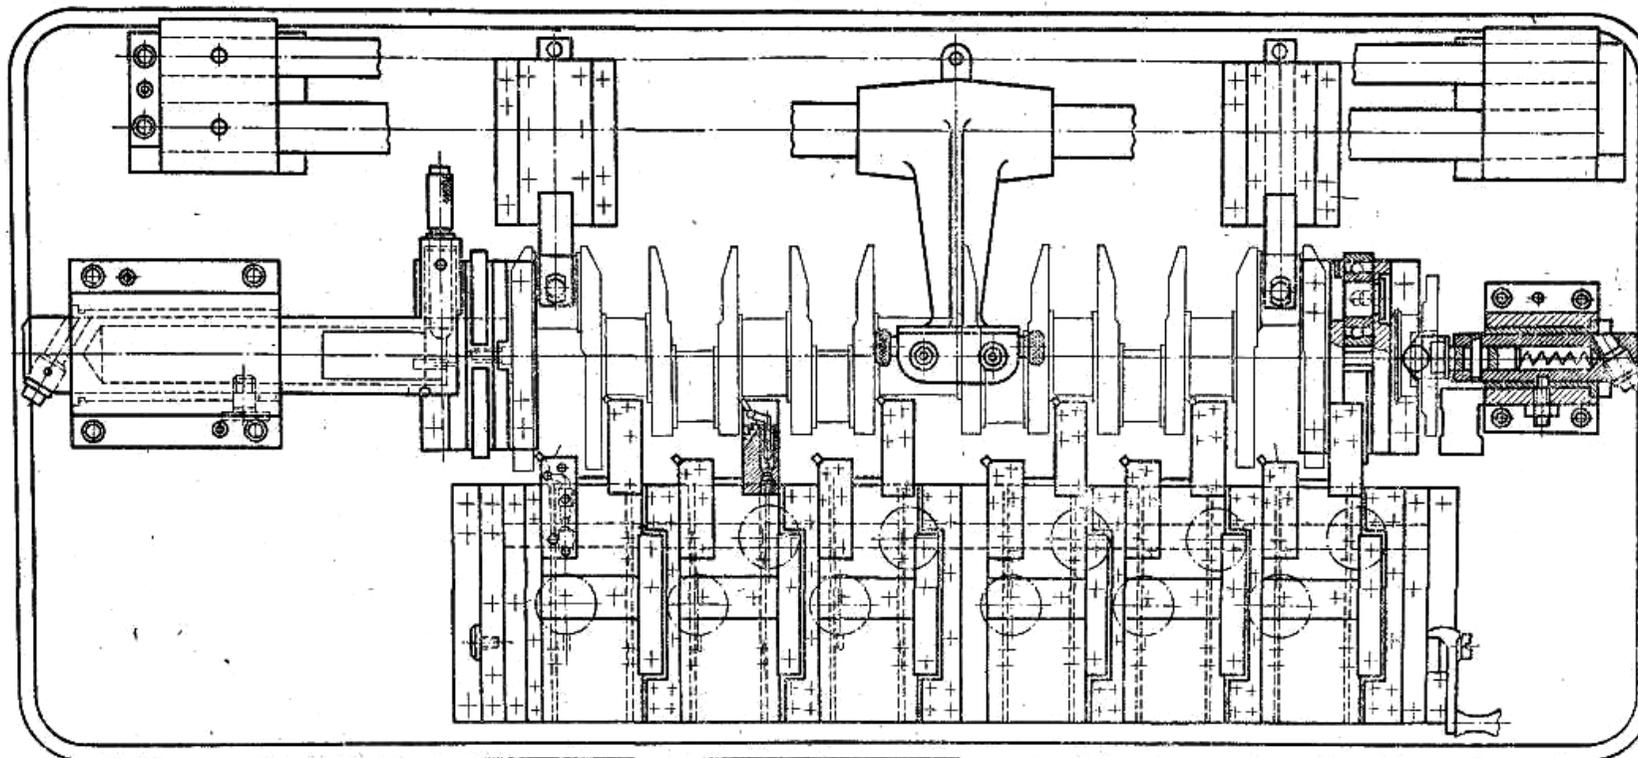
Приспособления для комплексного контроля коленчатого вала
